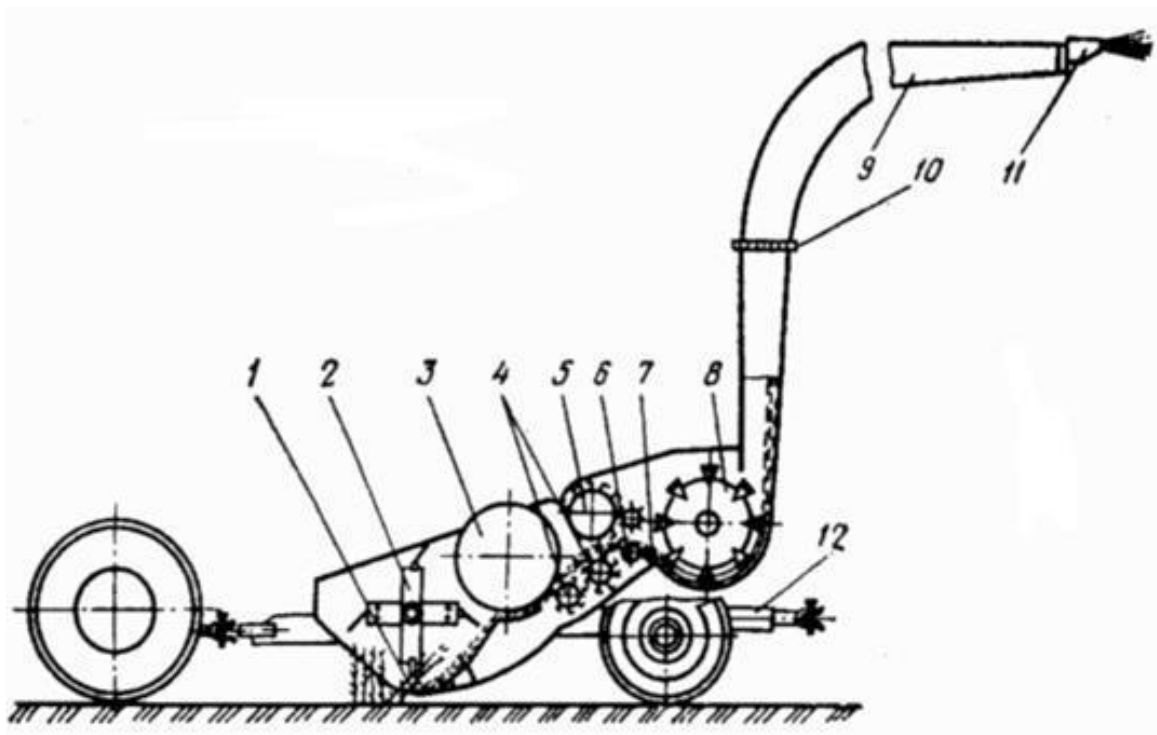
Технологический пресс прицепного кормоуборочного комбайна КПКУ-75: 1 – режущий аппарат; 2 – мотовило; 3 – шнек; 4 – передние вальцы; 5 – подпрессовывающий валец; 6 – гладкий валец; 7 – противорезущий брус; 8 – измельчающий барабан; 9 – силосопровод; 10 – механизм поворота; 11 – направляющий козырек; 12 – рама.
